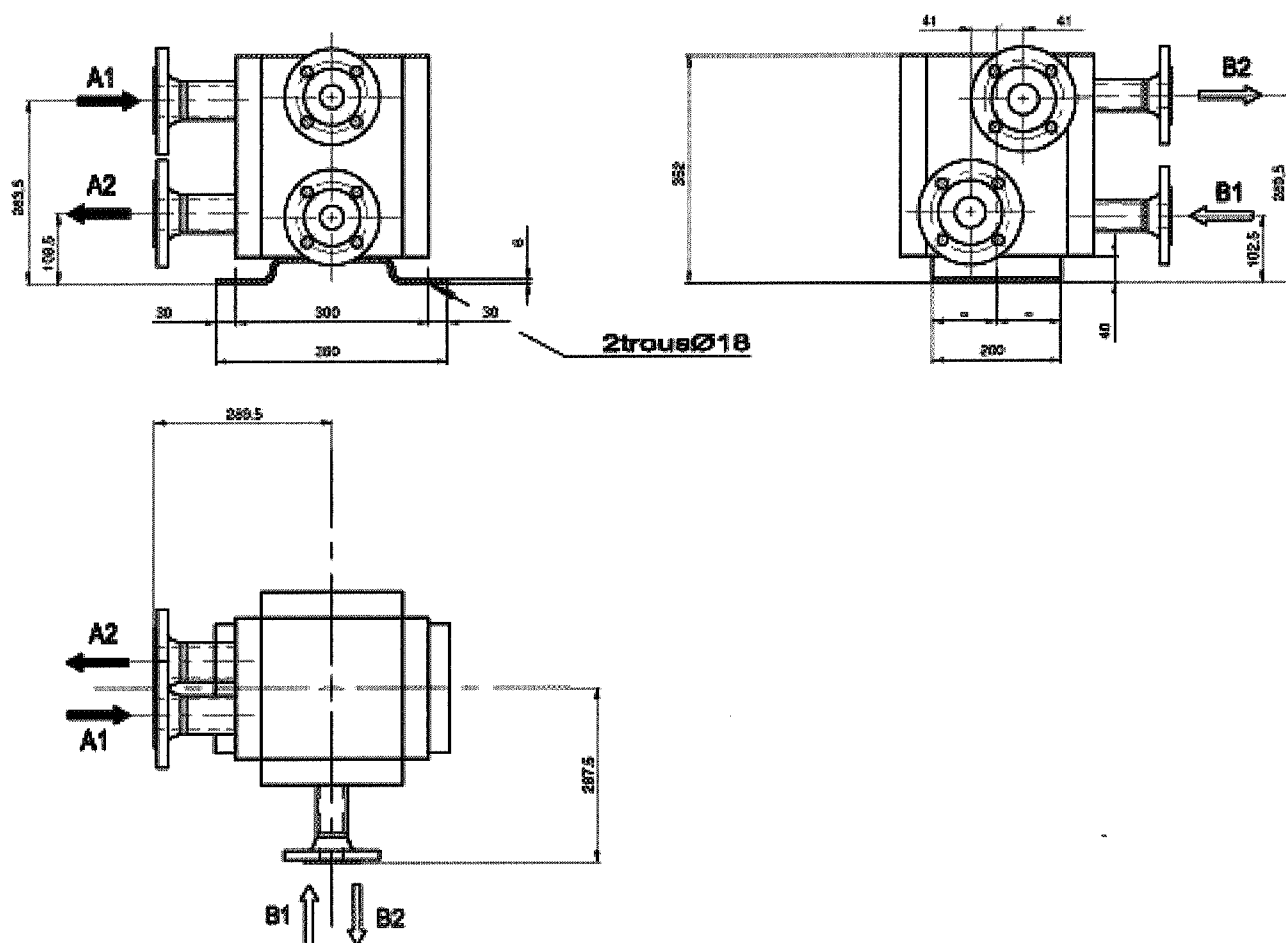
Габаритный чертеж теплообменника KPL41AC001
